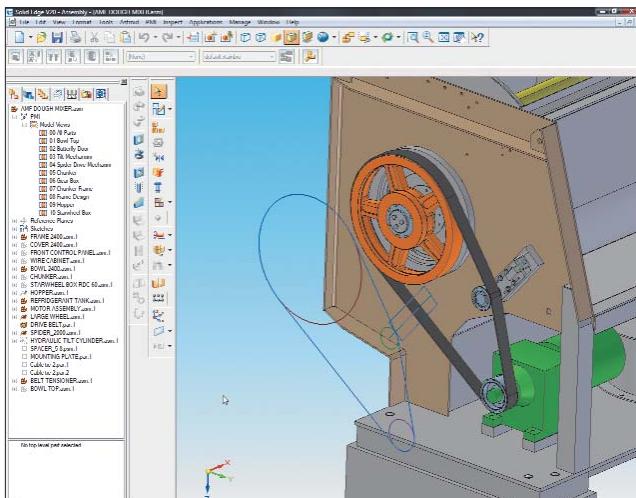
Взаимное расположение ремня и шкивов: позиция шкива с натяжным механизмом получена из эскиза сборки. Для этого используется имеющийся в Solid Edge гибридный метод 2D/3D-компоновки сборки
